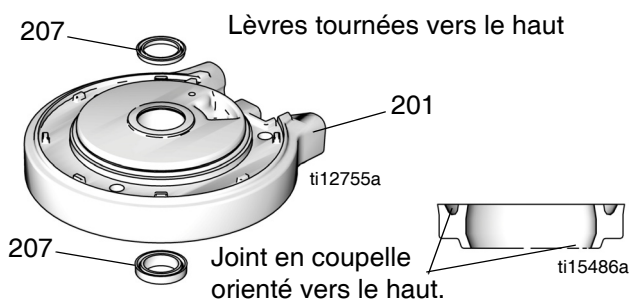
Installation du joint en coupelle du moteur pneumatique
